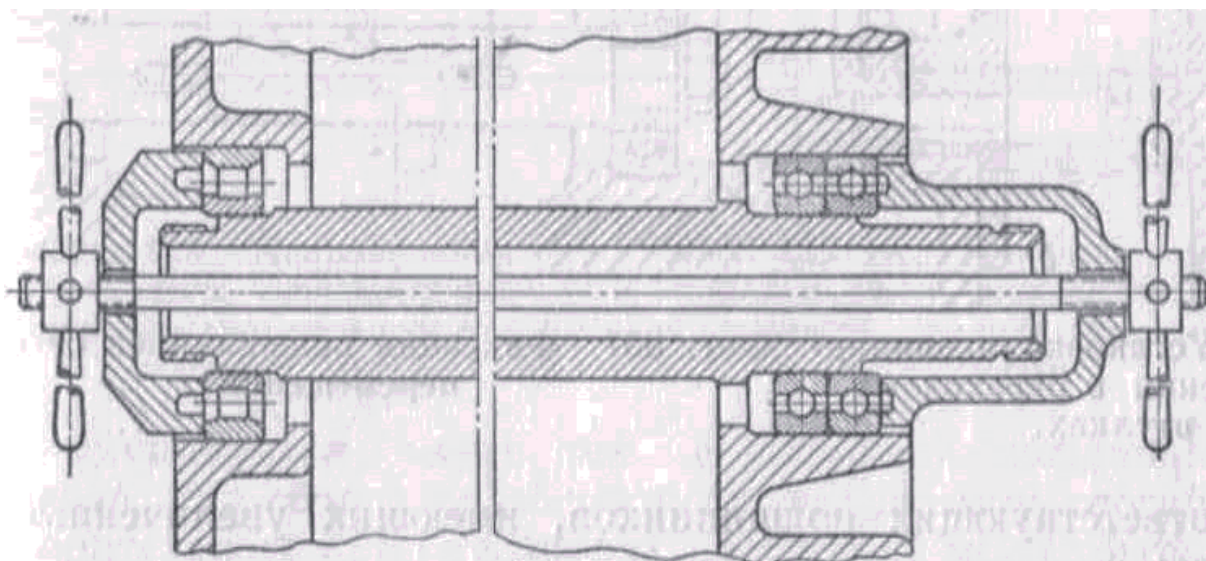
Приспособление для одновременной запрессовки подшипников на вал и в корпус
